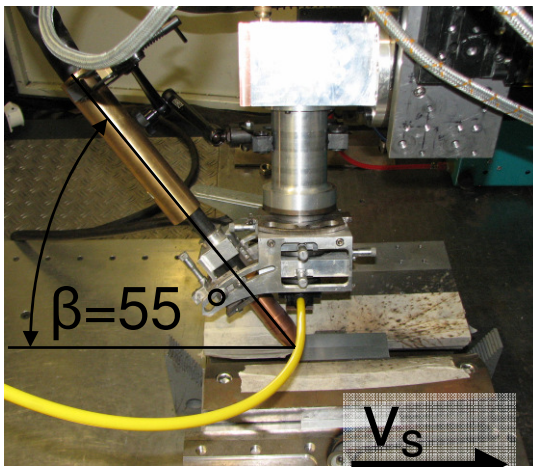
Ansicht des Versuchsaufbaus quer zur Schweißrichtung
